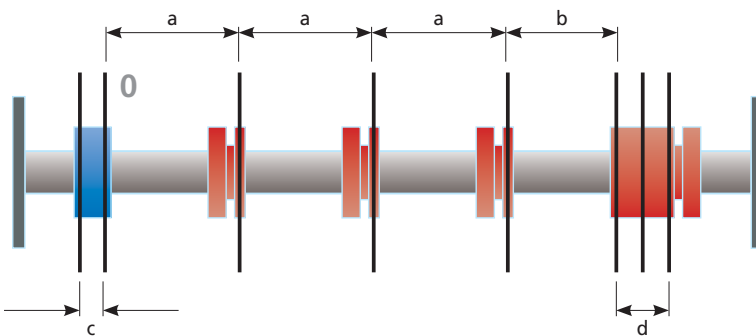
Verstellbarer Einhang mit einer festen und vier beweglichen Sägebüchsen
